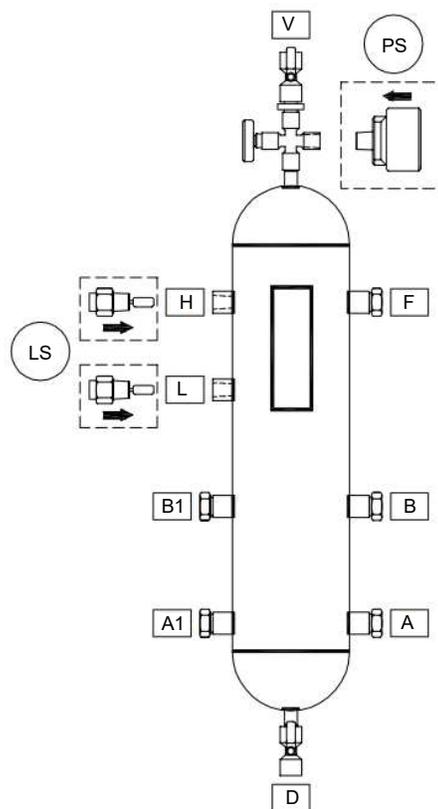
Montaje de interruptores del Plano 52 de tuberías
